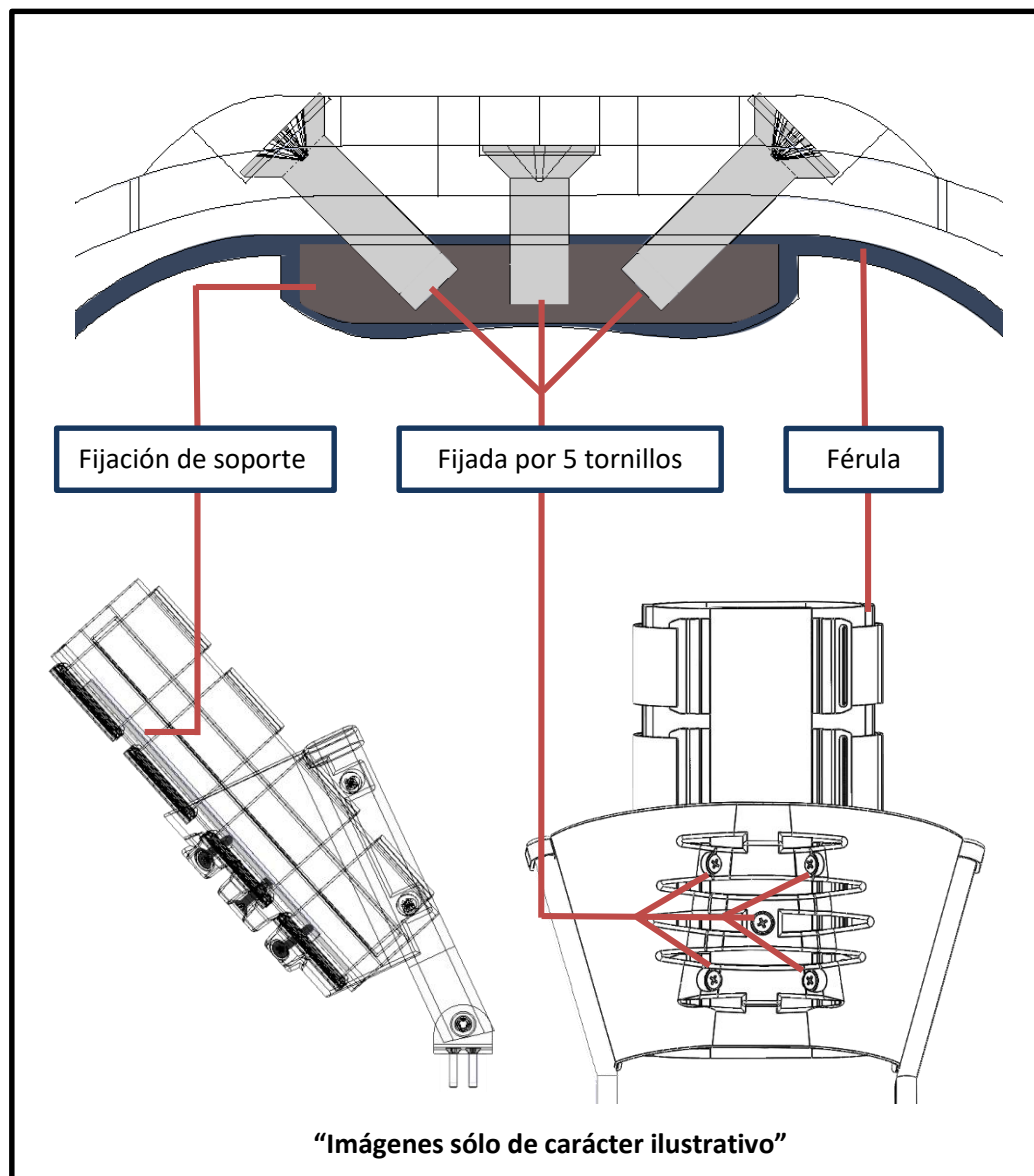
Vista detallada de protección de muslo/pantorrilla.
